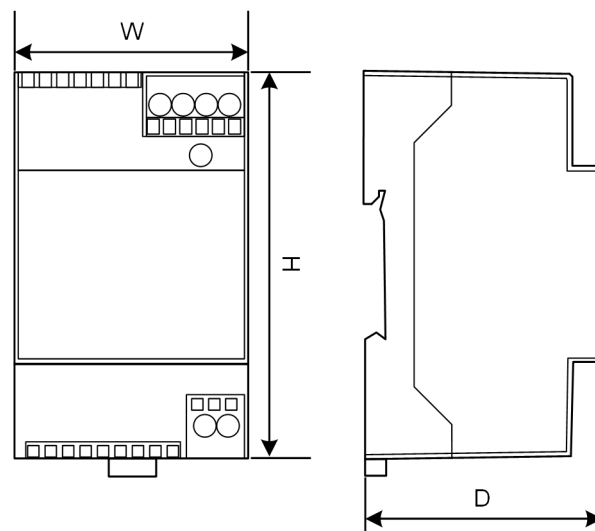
Skematisk fremstilling, dimensioner i millimeter
